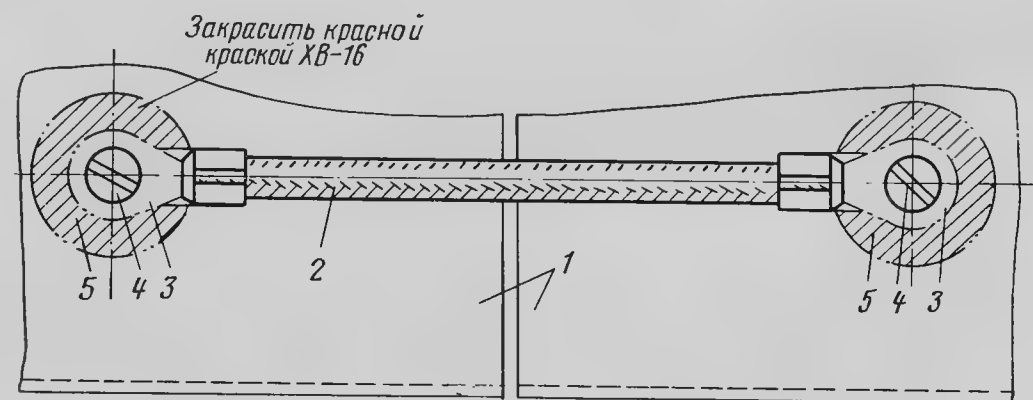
Типовая маркировка перемычки металлизации: 1 — детали конструкции; 2 — перемычки металлизации; 3 — наконечник; 4 — болт; 5 — очищаемая поверхность $d=25$ мм
